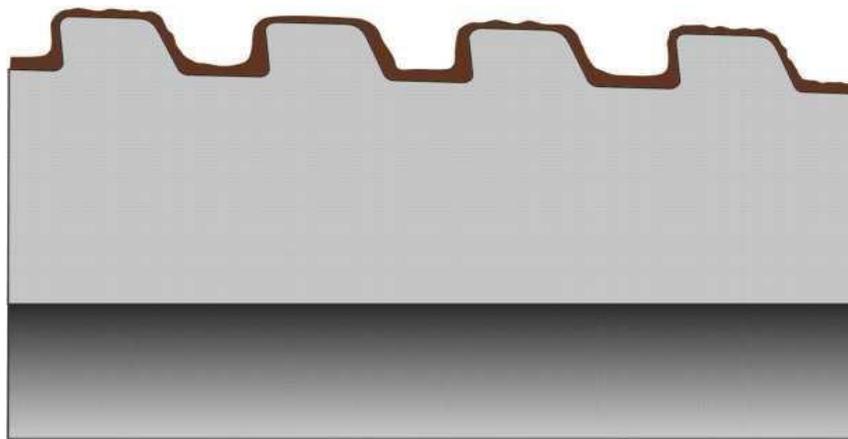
Размещение резьбовой смазки по профилю резьбы
